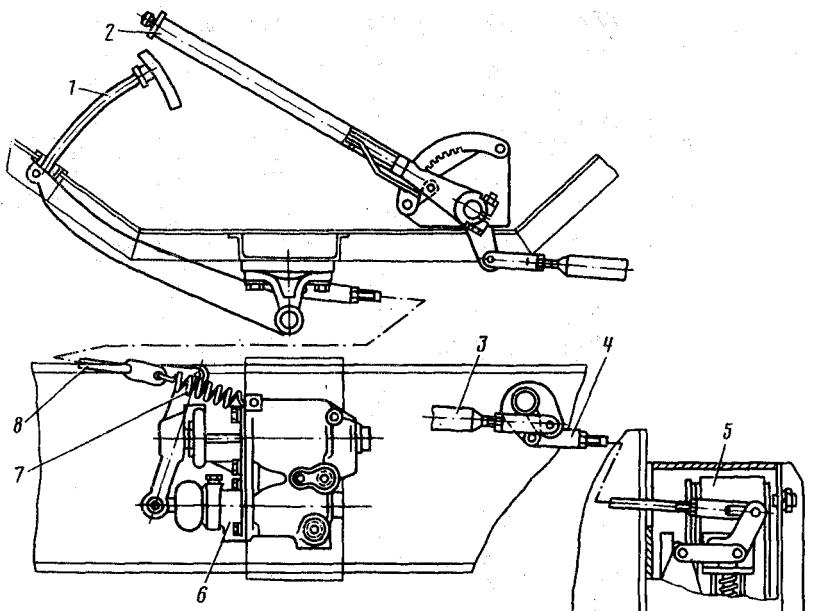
Ручной тормоз скрепера ДЗ-11П (схема привода)
